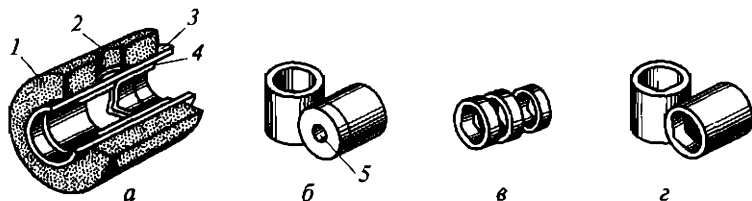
Патрон ПА для термитной сварки (а) и детали к нему: алюминиевые колпачки к патрону (б), алюминиевые шайбы (в) и втулки (z): 1 — термитный муфель; 2 — литниковое отверстие; 3 — стальной кокиль; 4 — втулка; 5 — отверстие в доннышке втулки для контроля глубины вхождения в него жил
